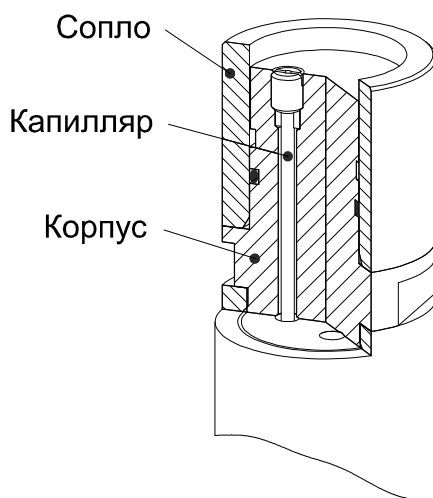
Положение капилляра в корпусе сопла калибратора
